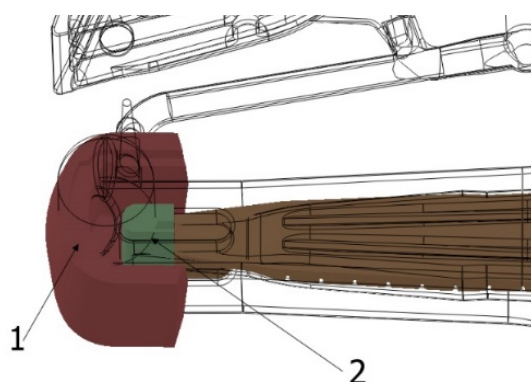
Расположение стержней в форме для типичных мест образования ГТ в отливке «Корпус автосцепки»
